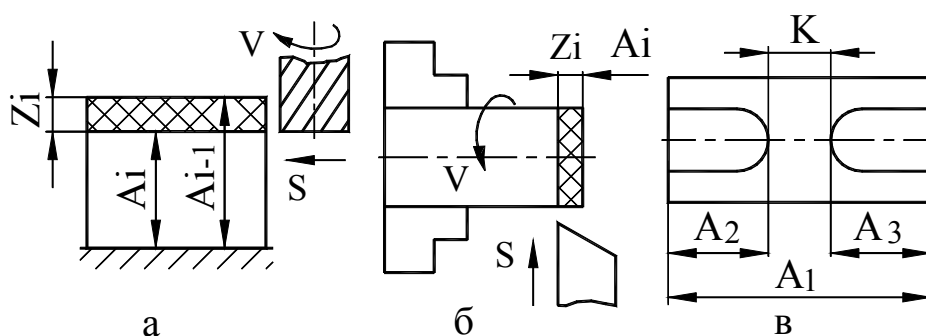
Виды технологической размерной цепи: а – припуск – замыкающее звено; б – припуск – технологический размер; в – конструкторский размер – замыкающее звено
